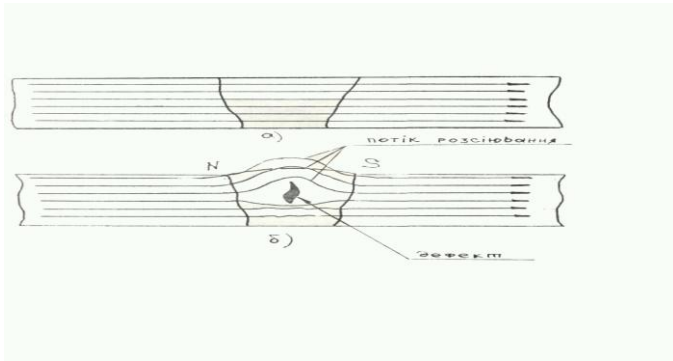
Розташування магнітного потоку по перерізу якісного (а) і дефектного (б) зварного з'єднання
